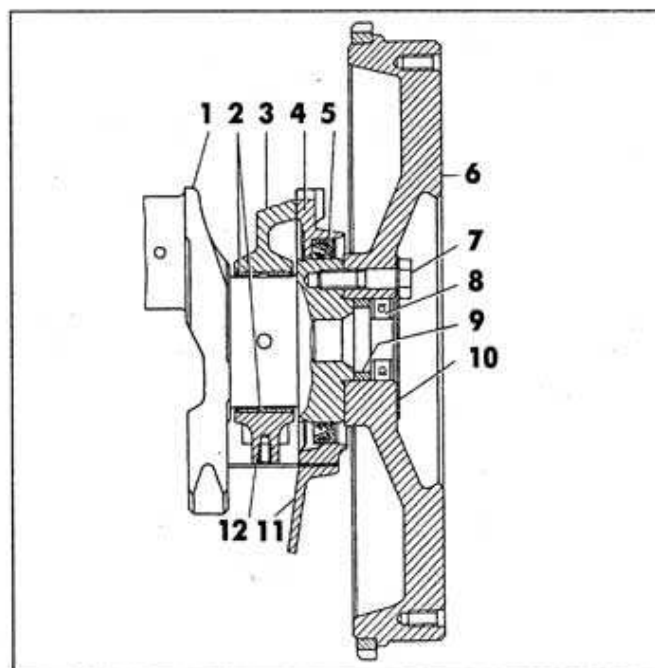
Задний конец коленчатого вала: 1 – коленчатый вал; 2 – вкладыши подшипника; 3 – блок цилиндров; 4 – сальникодержатель; 5 – сальник; 6 – маховик; 7 – болт крепления маховика; 8 – подшипник; 9 – распорная втулка; 10 – шайба болтов маховика; 11 – масляный картер; 12 – крышка подшипника
